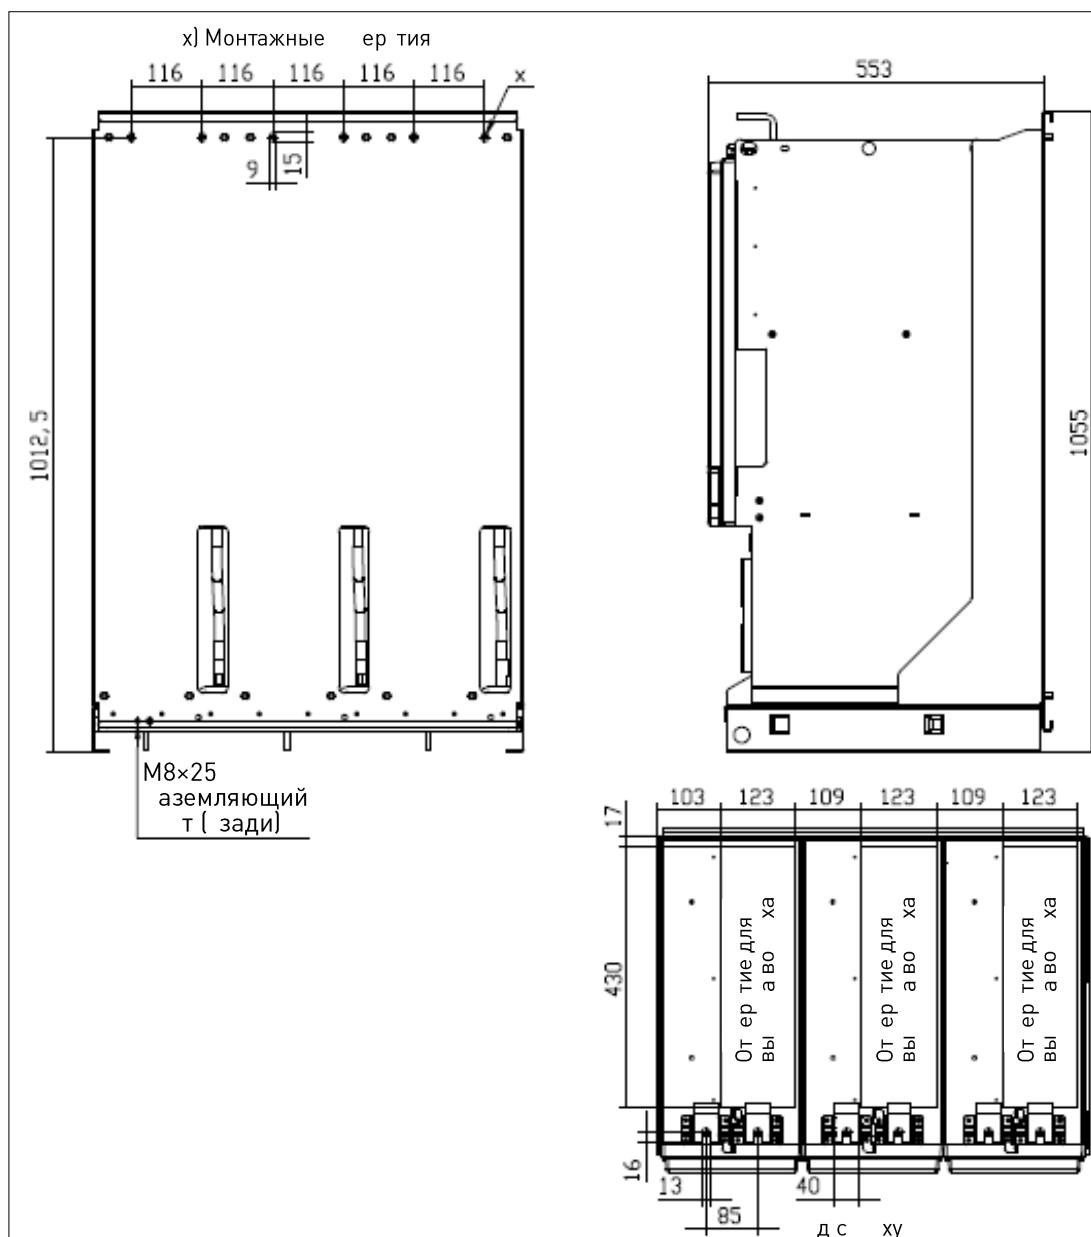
Габариты инвертора VACON® NXI, типоразмер FI13 (вид сзади).
